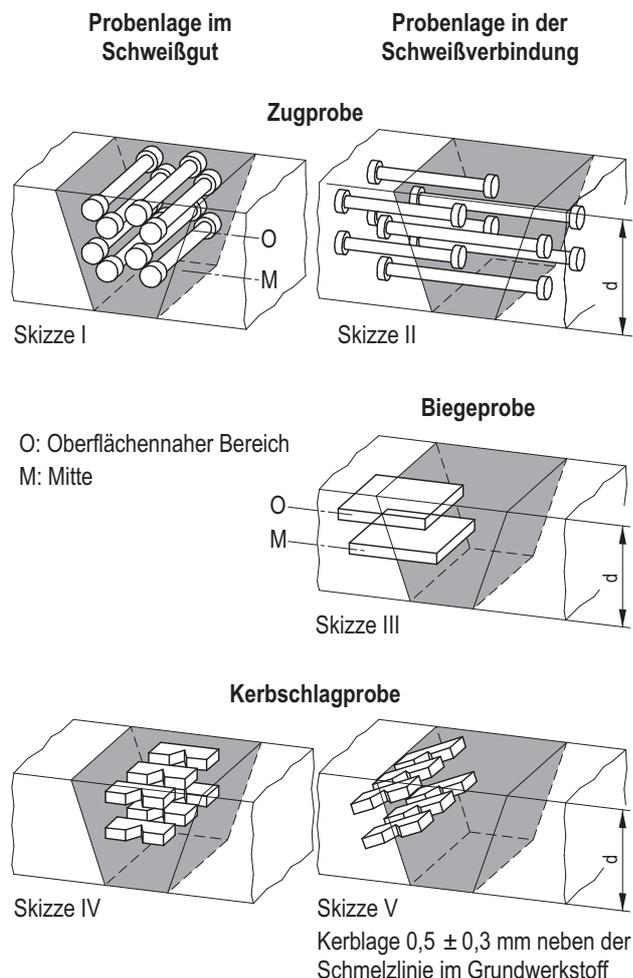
Probenentnahme bei Verfahrensprüfungen für Durchbruchschweißungen
